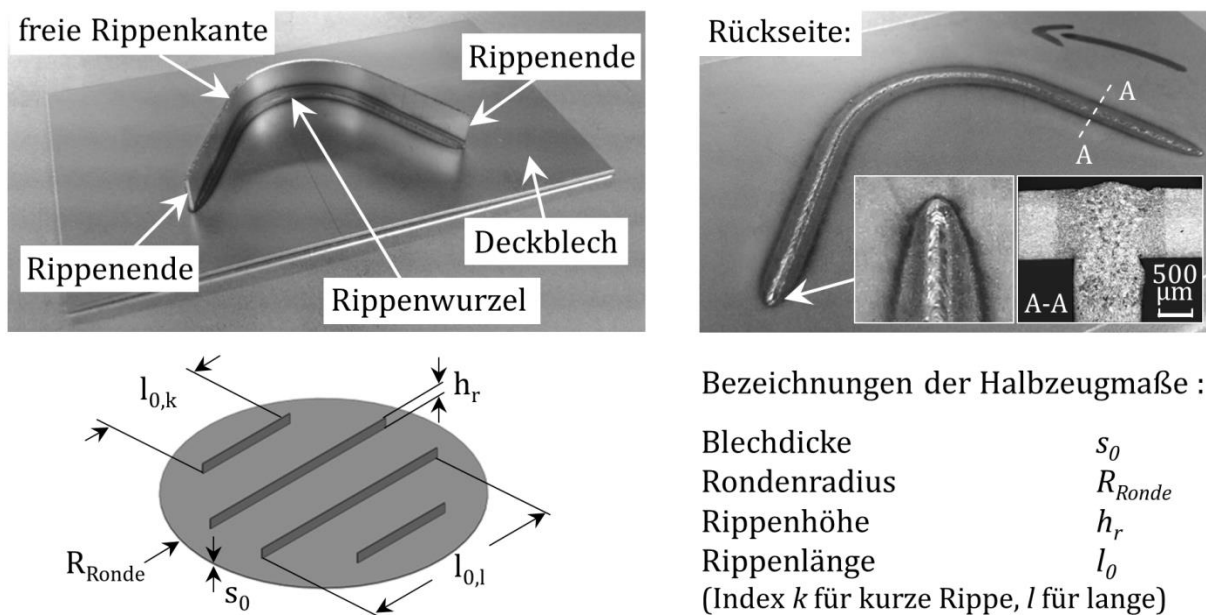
Begriffliche Definitionen zur Beschreibung lasergeschweißter Rippenblechhalbzeuge am Beispiel einer Probe aus [S-Gaw14] (oben) und einem Halbzeug zur HBU mit Form 2 (unten).
